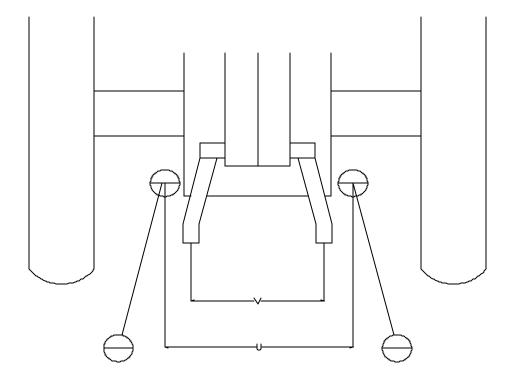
Prueba de levante – Geometría del enganche de tres puntos
